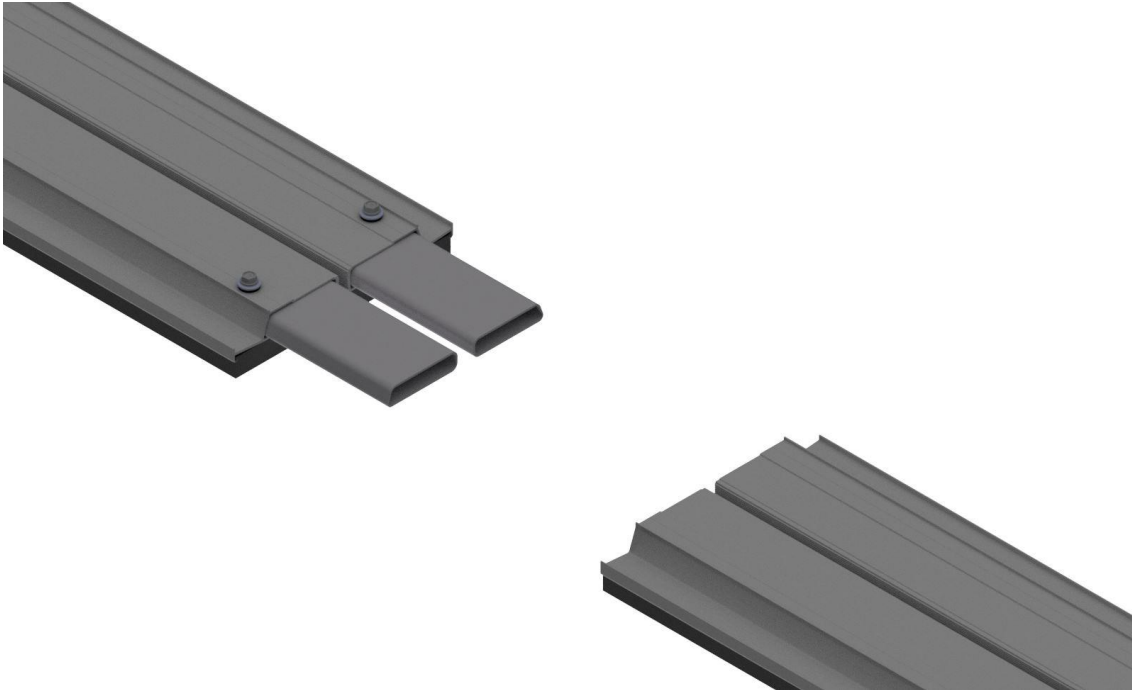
Stoßverbinder mit je einer Dünnschraube fixieren
